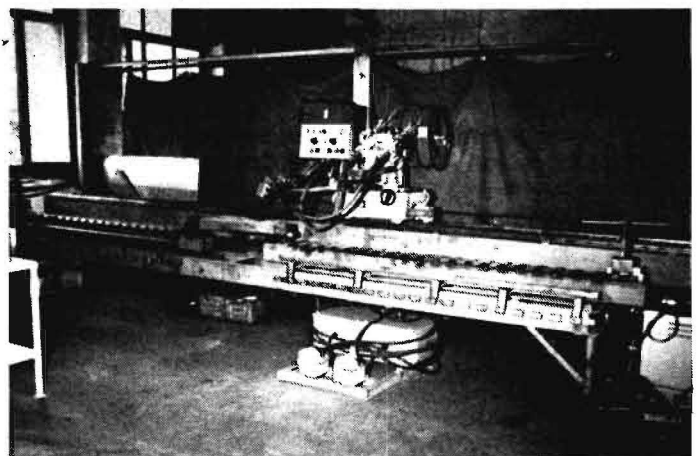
Sondermaschine zum teilautomatisierten Schweißen der Querträger für die Hochdruckpresse K 453
